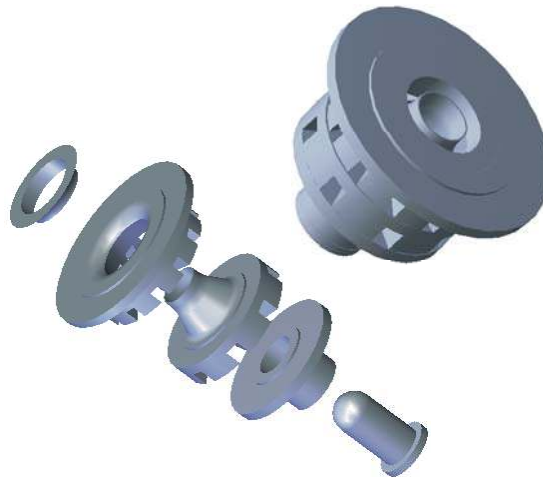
Drallerzeuger Typ A, Drallerzeugung mittels tangentialer Kanäle
